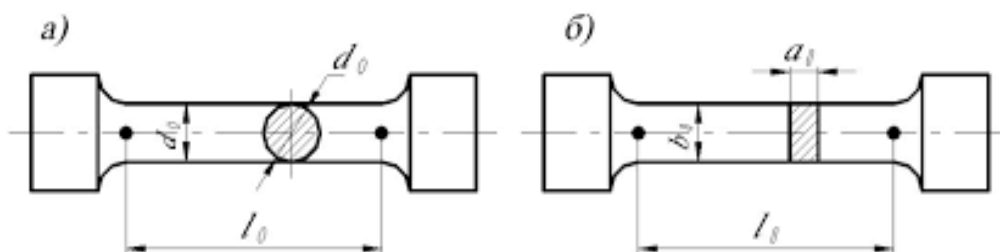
Стандартный образец для испытаний на одноосное растяжение
